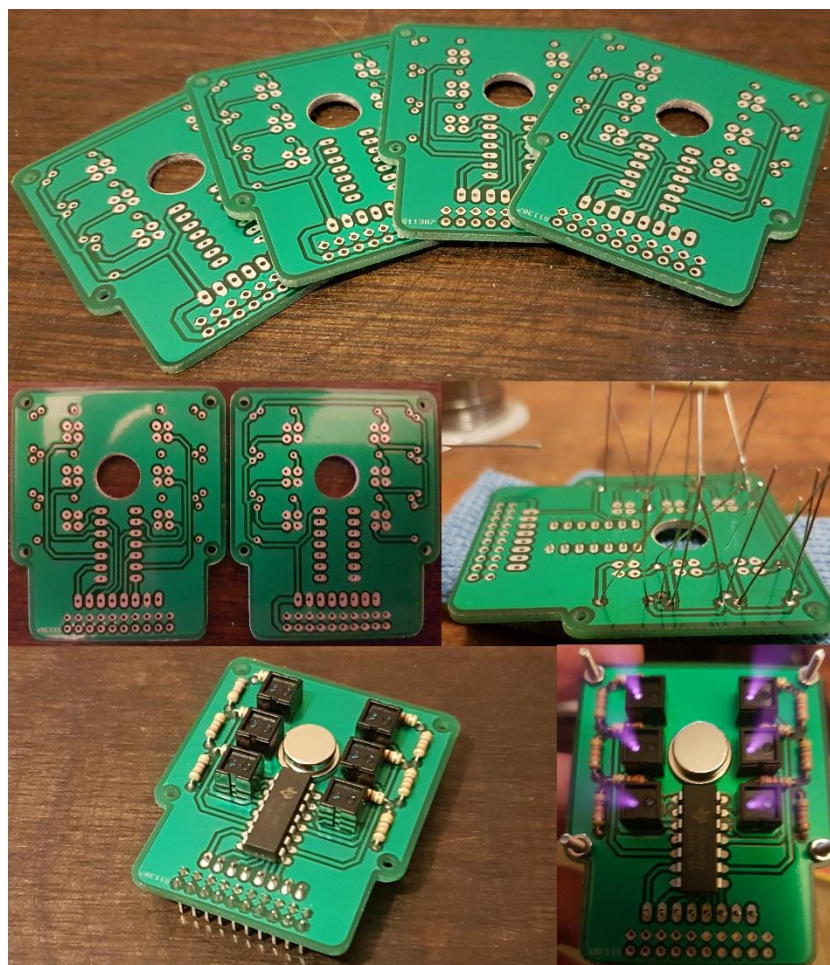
Vista de la capa superior e inferior del diseño PCB
